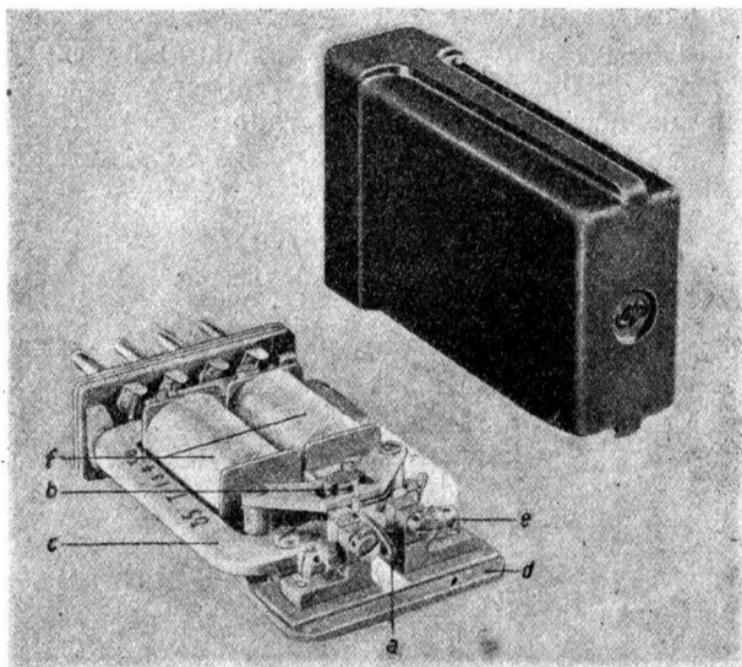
Aspecto de un relevador Siemens. (Desprovisto de cubierta que se ve a un lado)
